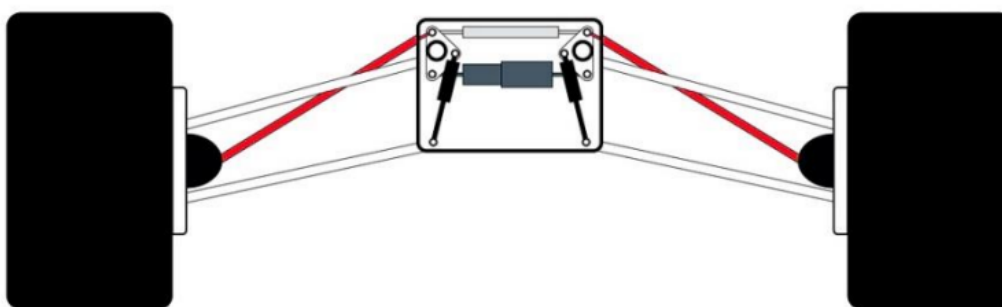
Кінематична схема підвіски типу Pull Rod
